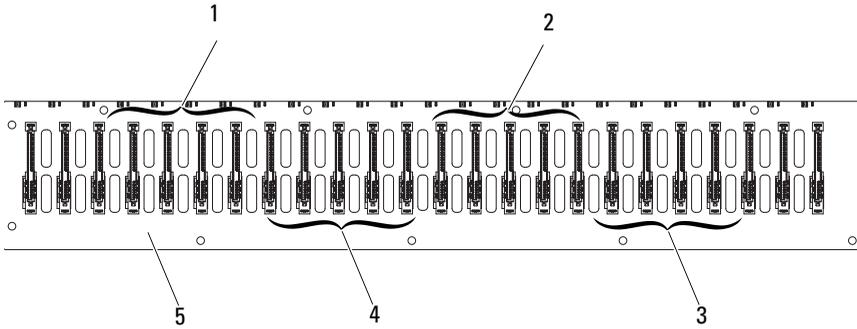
Rückansicht der Rückwandplatine
